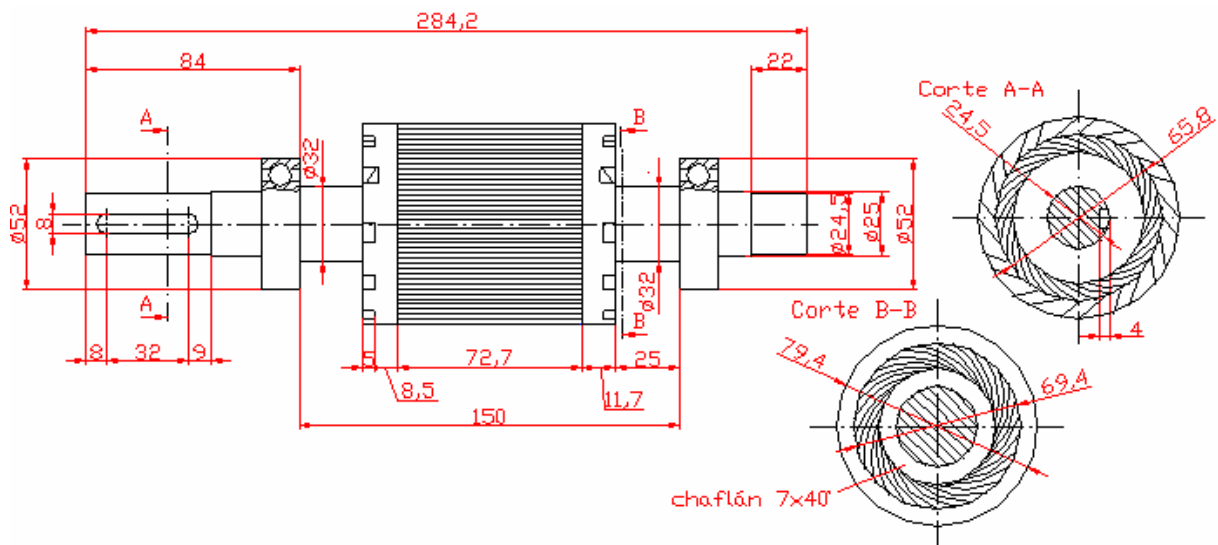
Vista lateral y en planta del rotor de chapas prototipo II. Las cotas están dadas en mm.
